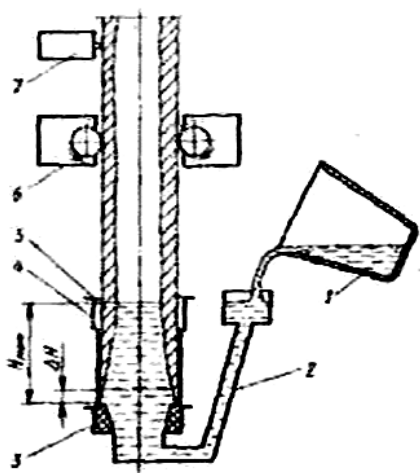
Схема непрерывного литья намерзанием: 1-ковш; 2 – металлопровод; 3 – стакан; 4 – водоохлаждаемый кристаллизатор; 5 – корка отливки; 6-тянущее устройство; 7-устройство для отрезки отливки
